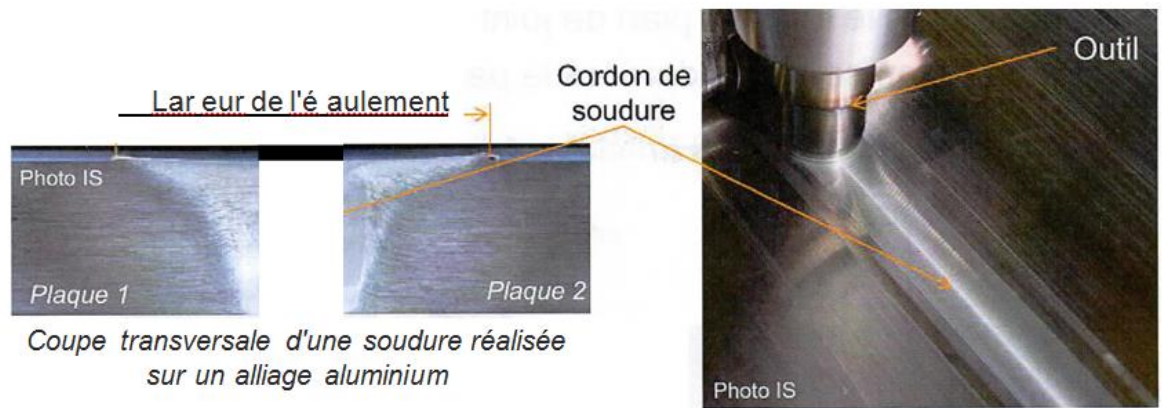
Coupe transversale d'une soudure réalisée sur un alliage d'aluminium
